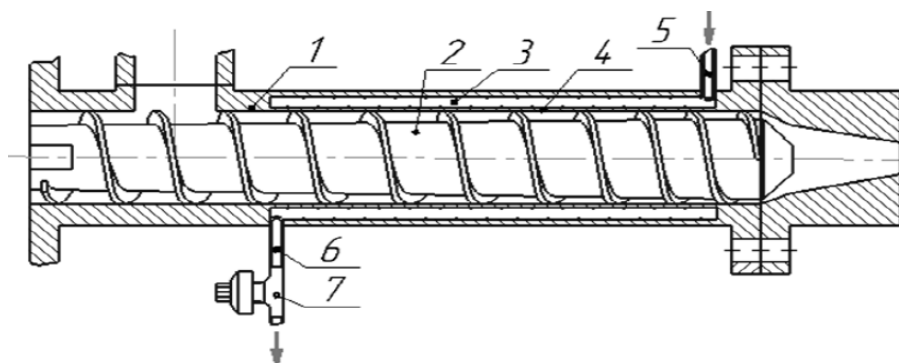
Узел плавления установки по переработке полиэтилена и полипропилена: 1 - корпус установки; 2 - шнек; 3 - нагреватель, выполненный в виде полого цилиндра; 4 - зона плавления; 5 - патрубок подвода пара; 6 - патрубок отвода конденсата; 7 - конденсатоотводчик
